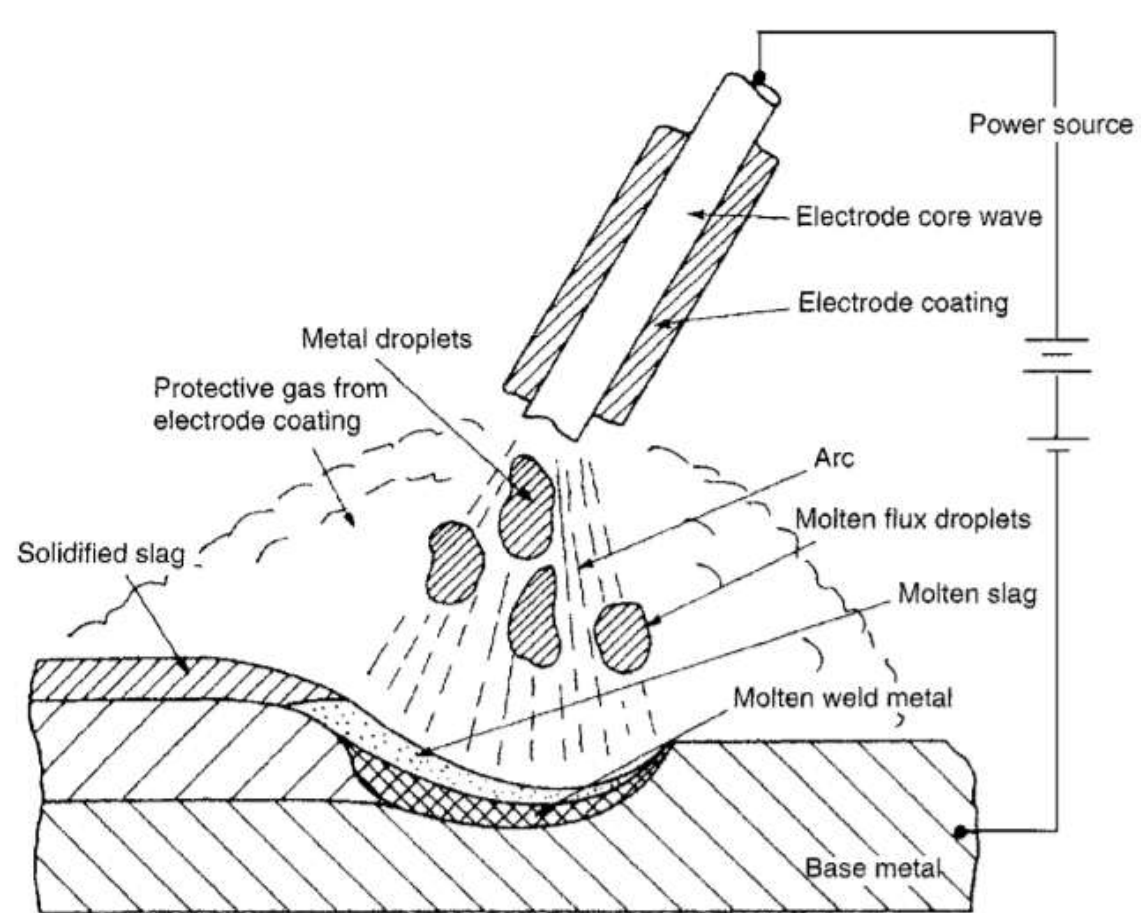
Схема сварочной дуги как источника теплоты:
